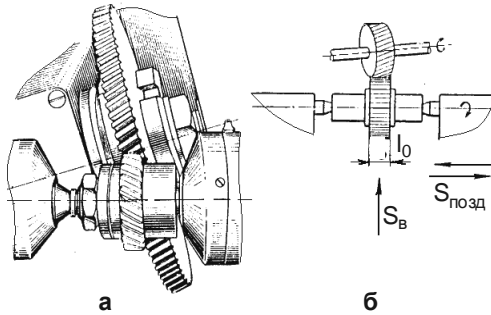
Шевінгування циліндричного зубчастого колеса дисковим шевером: а – загальний вигляд (подача поздовжня); б – схема шевінгування із вертикальним переміщенням столу верстата
